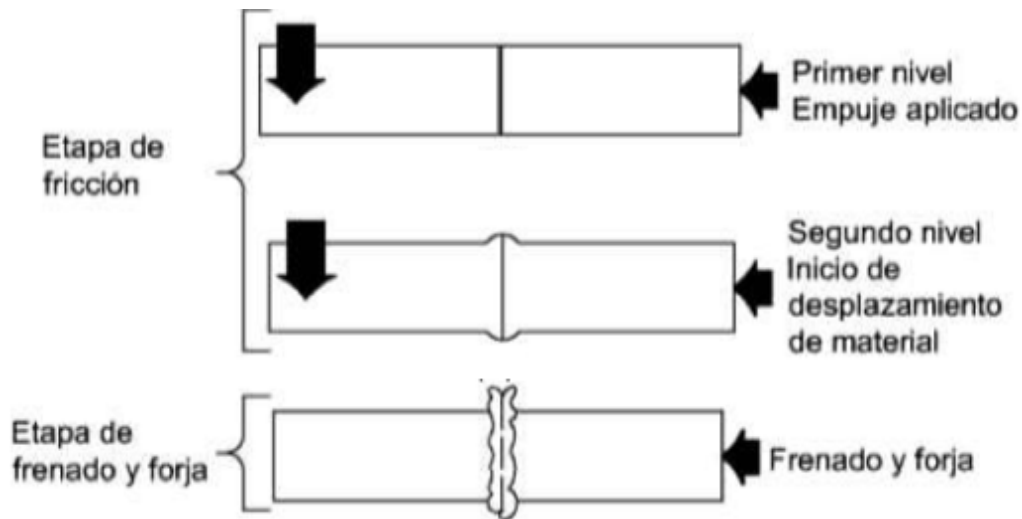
Etapas del proceso de soldadura por fricción
